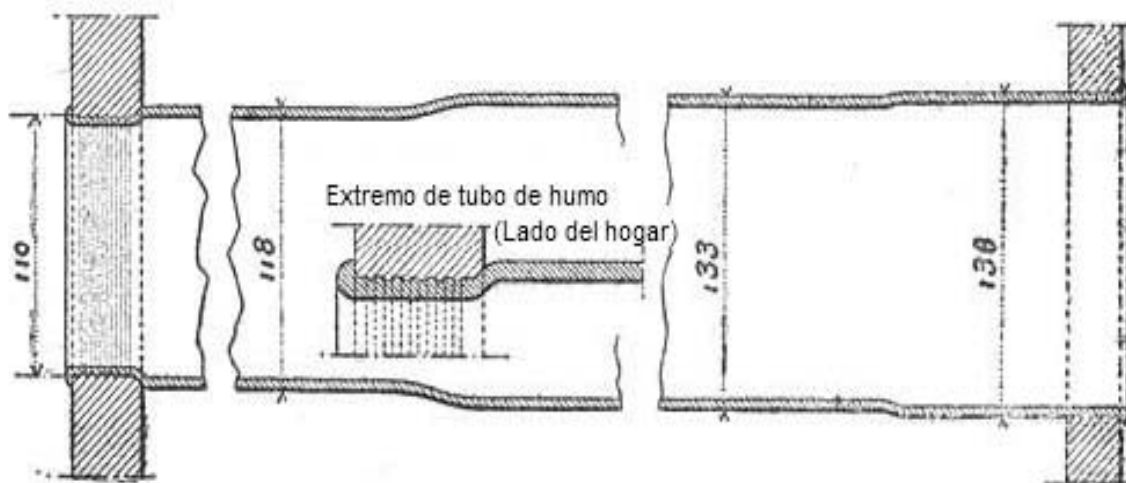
Tubo grande para recalentador (Est). Montaje sobre placa tubular del hogar en cobre.
